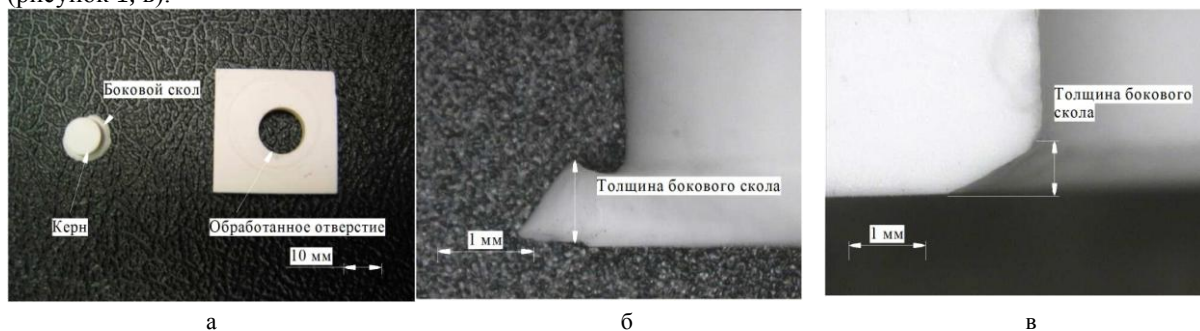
Боковые сколы, возникающие при алмазном сверлении: а – две части обработанной заготовки; б – вид сбоку на керн; в – вид сбоку на отверстие
